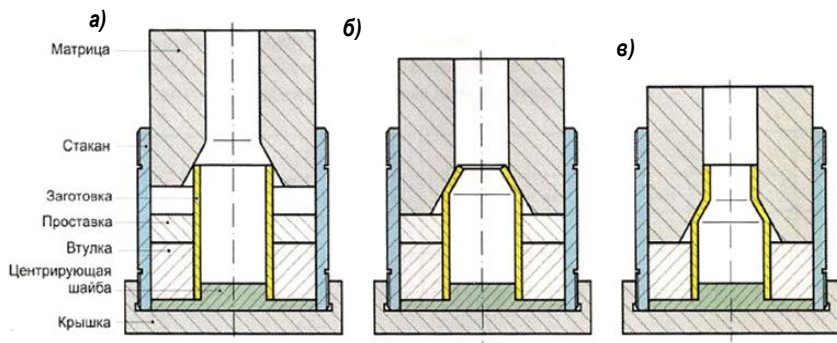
Специальное приспособление для обжима: а – заготовка; б – обжим на конус; в – обжим на цилиндр
